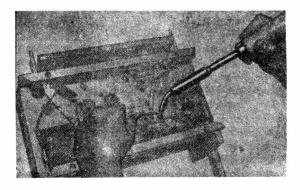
Manera de colocar el soldador y el estaño para hacer soldadura al chasis.
